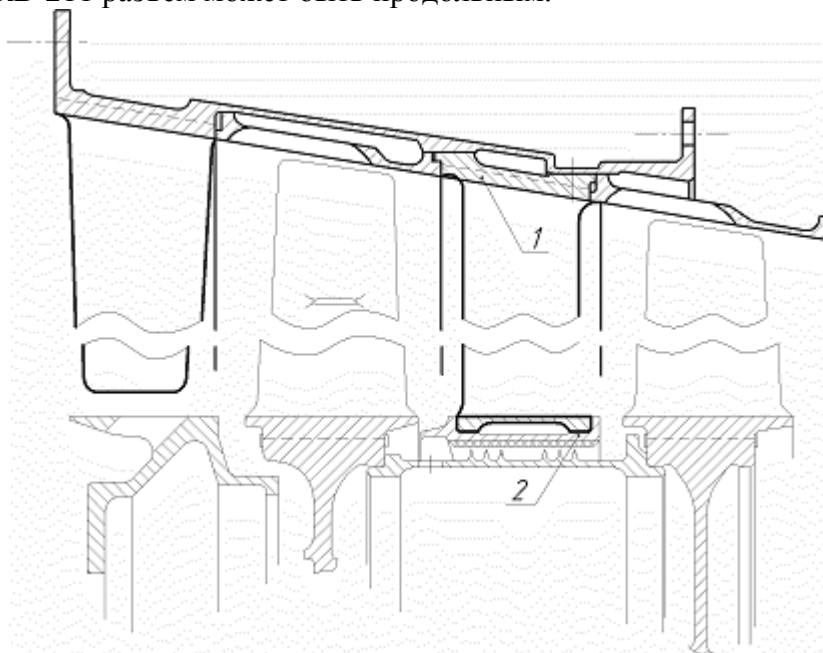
Разборный НА компрессора СД ТРДД НК-56 (крепление лопаток в наружном кольце замком «ласточкин хвост» с предварительной установкой в канавку внутреннего кольца:
